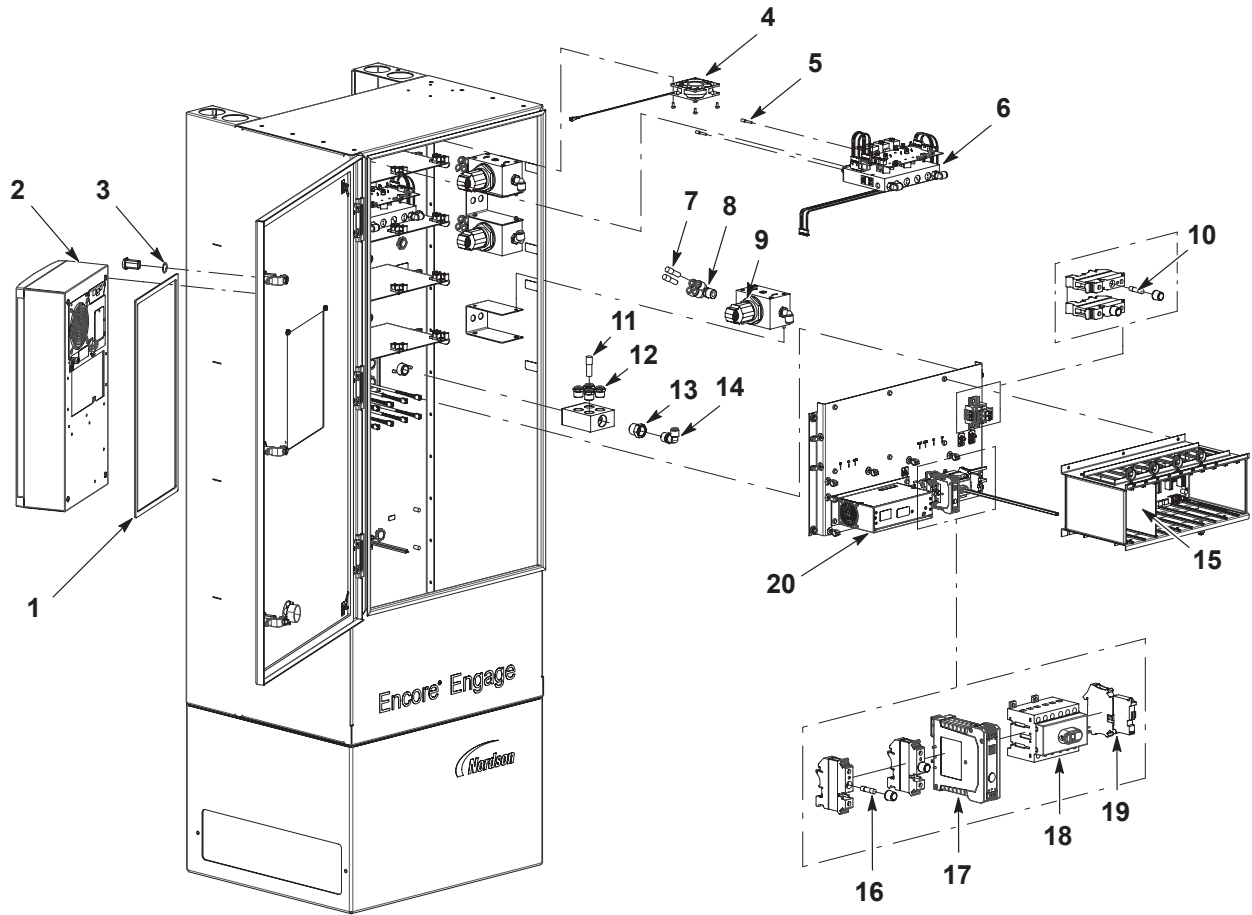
Komponenten der Zusatzsteuerung mit Kühlgerät, 1 von 2
